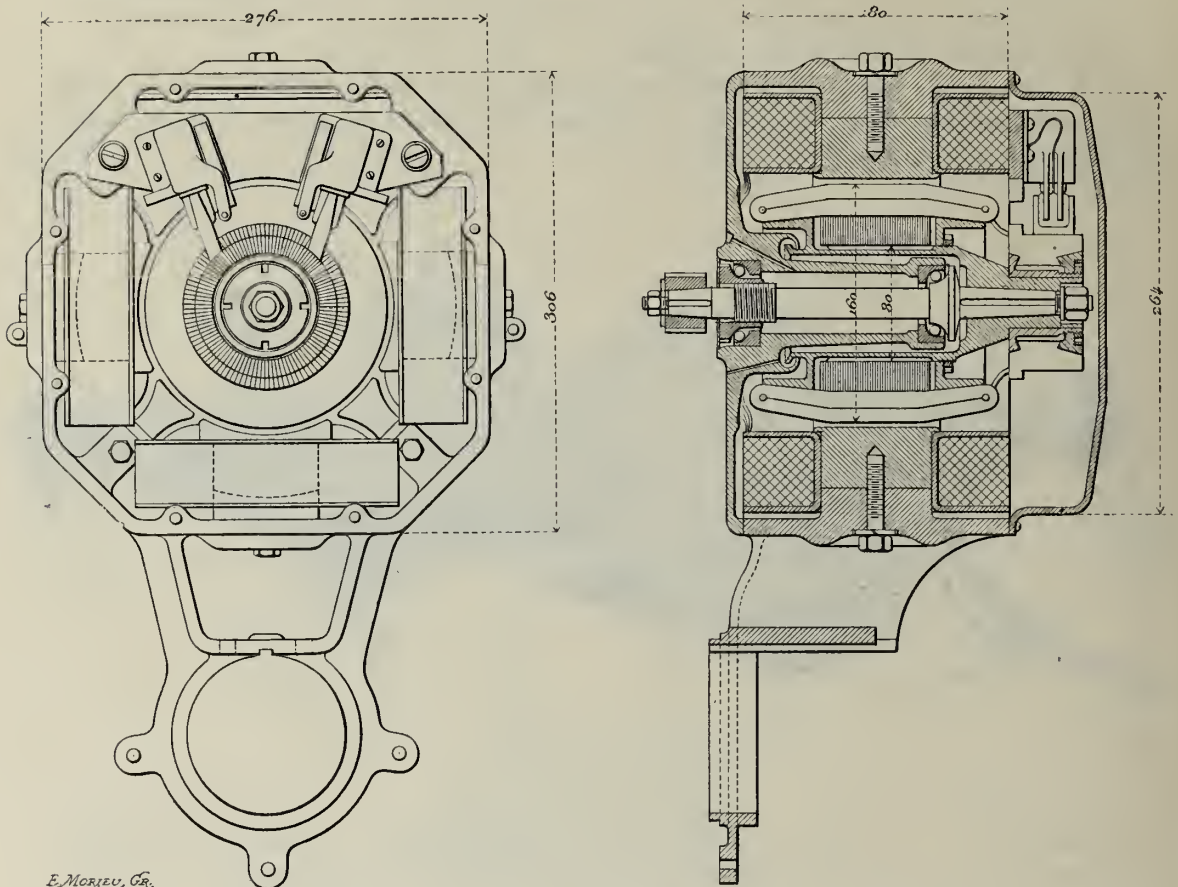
Vue en élévation et vue en coupe verticale du moteur Kriéger.
